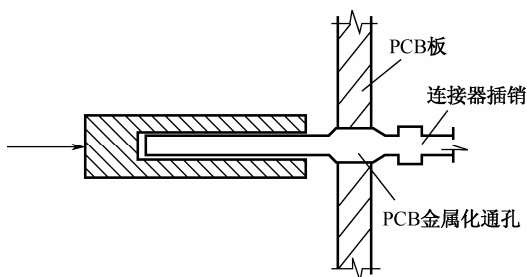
连接器插销和 PCB 金属化通孔间的压接接续
